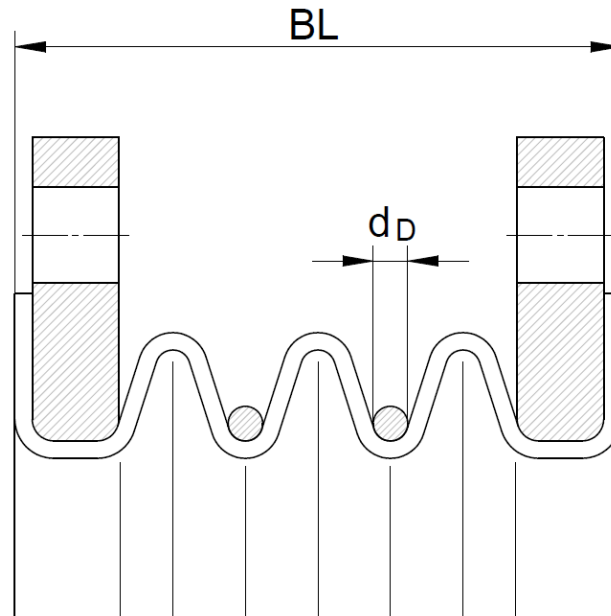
Skizze eines PTFE-Axialkompensators; Beispiel für 3-wellige Ausführung
